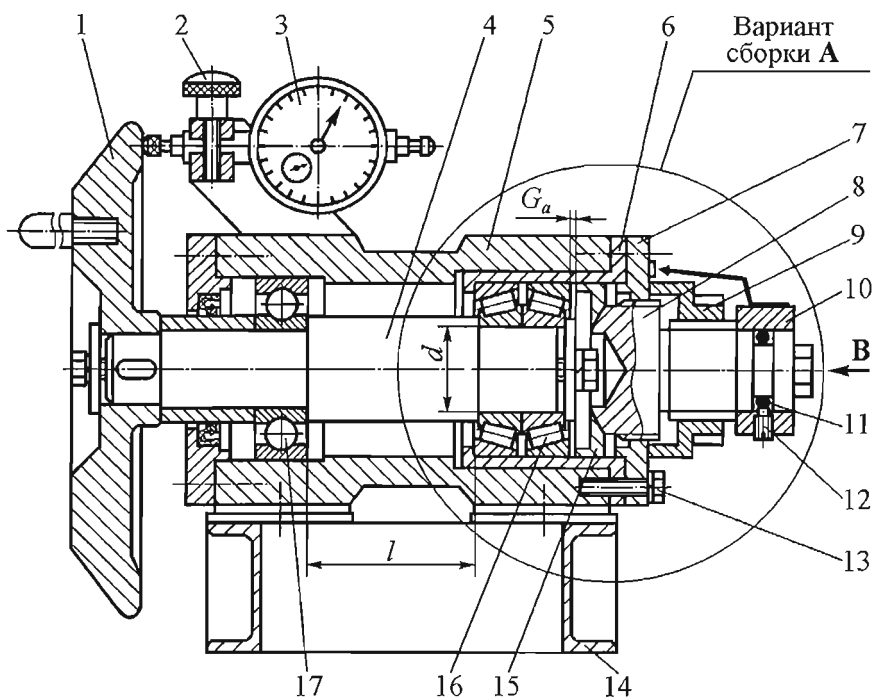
Конструкция лабораторной установки при установке подшипников по схеме I
